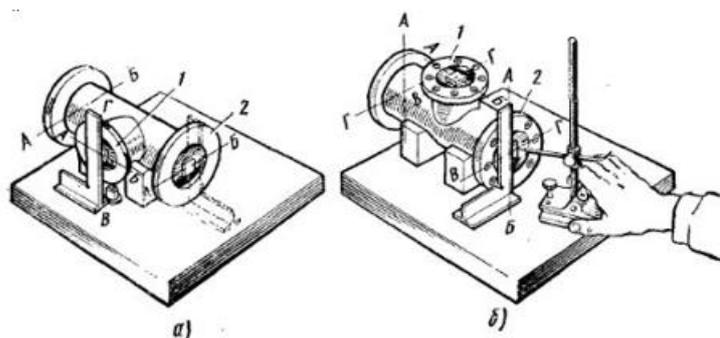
Разметка патрубка с перекантровкой: а — первое положение; б — второе положение
